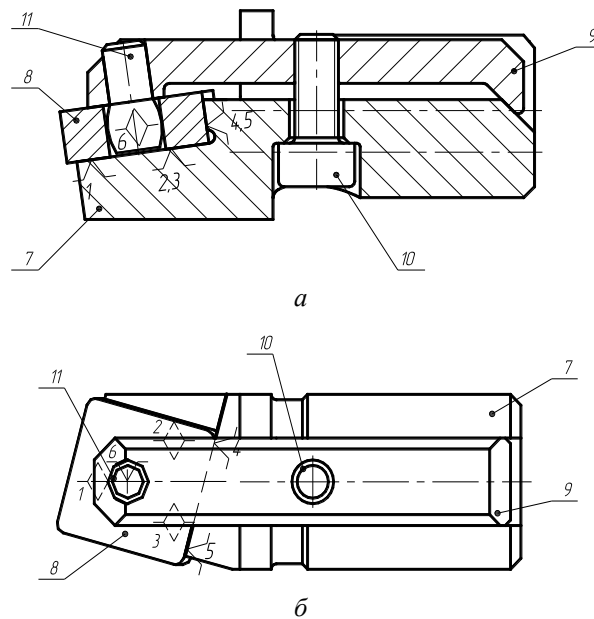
Резцовый блок: а – главный вид; б – вид сверху; 1, 2, 3 – установочная база, 4 и 5 – направляющая база, 6 – опорная база, 7 – корпус режущего инструмента, 8 – сменная режущая пластина, 9 – прихват, 10 – винт, 11 – штифт;
